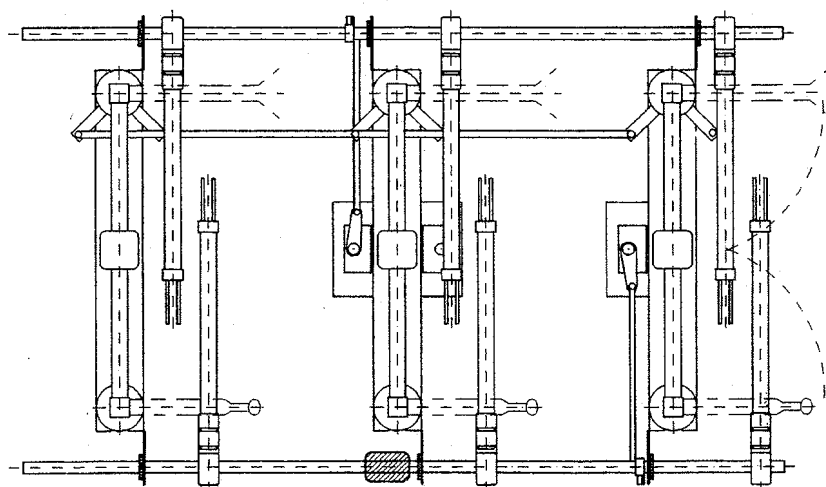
Параллельная установка трехполюсного двухколонкового поворотного разъединителя (основная конструкция)
